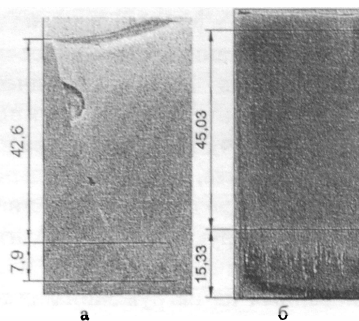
Макрошлифы поперечного сечения швов при сварке в нижнем положении с применением магнитного поля (а) и без него (б)
